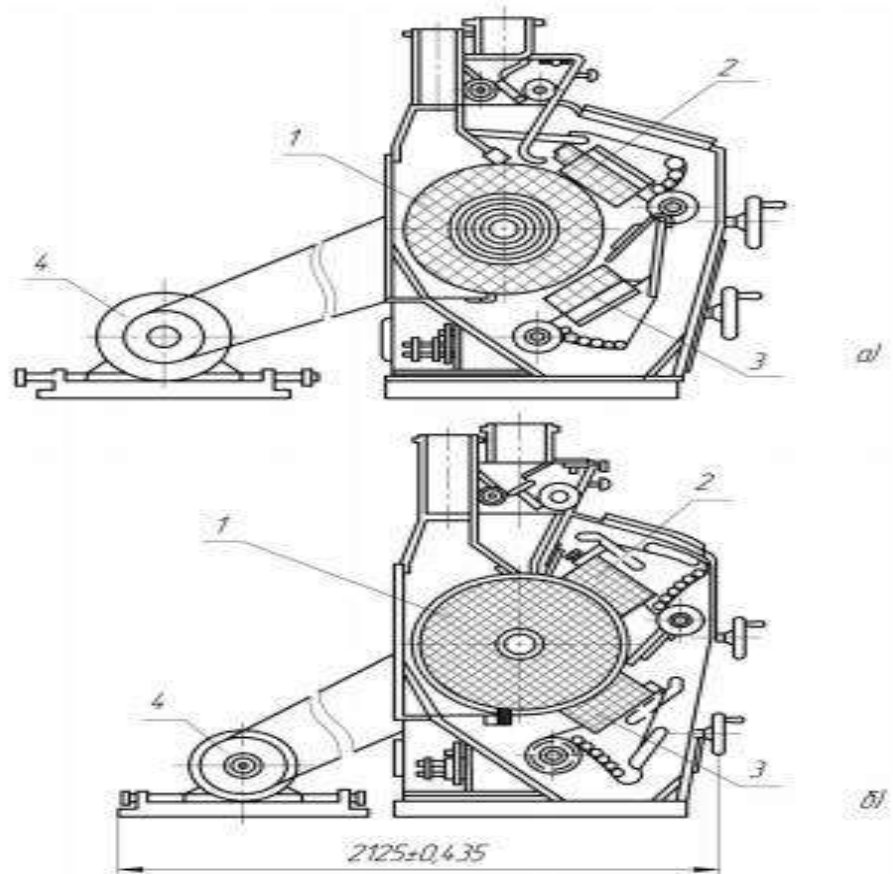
Дводековий лушильний верстат типу 2ДШС-3
